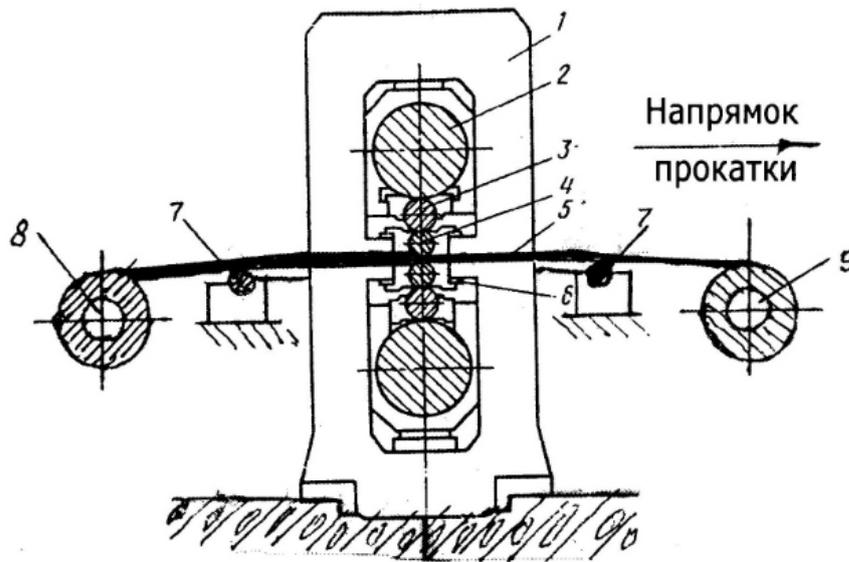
Реверсивний стан з кліттю HS: 1 – станина кліті; 2 – опорний валок; 3 – проміжний валок, 4 – робочий валок, 5 – штаба, 6 – протизгін валків, 7 – опорно- направляючі ролики, 8 і 9 – моталки.
